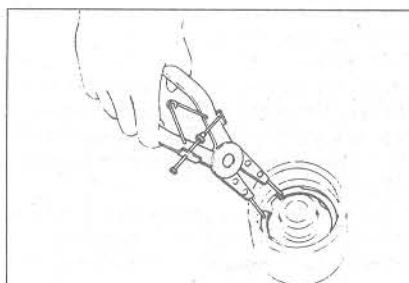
Извлечение стопорного кольца 'А' из поршня (Глава 25)
